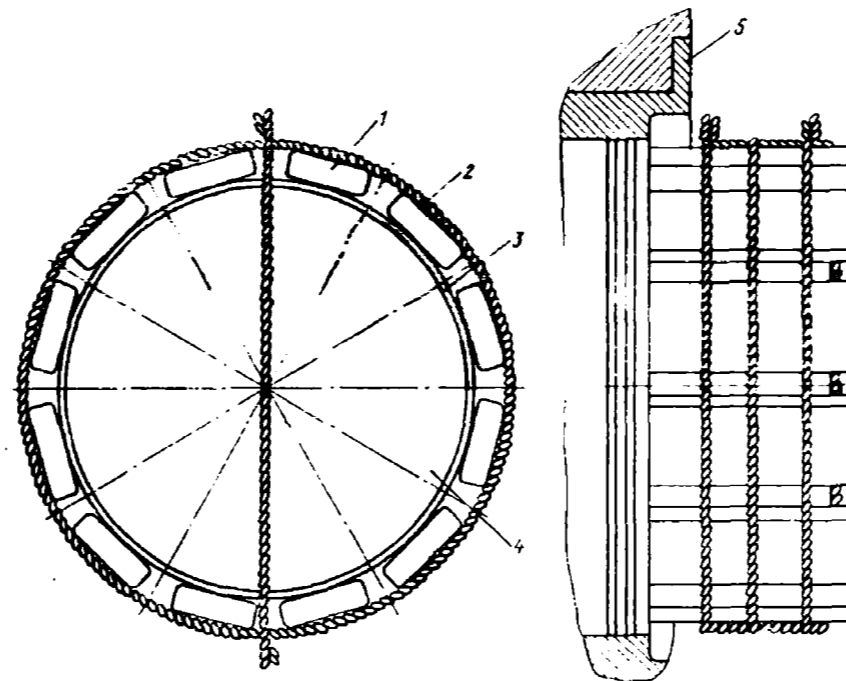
Упаковка носка коленчатого вала дизелей типа В-46:
